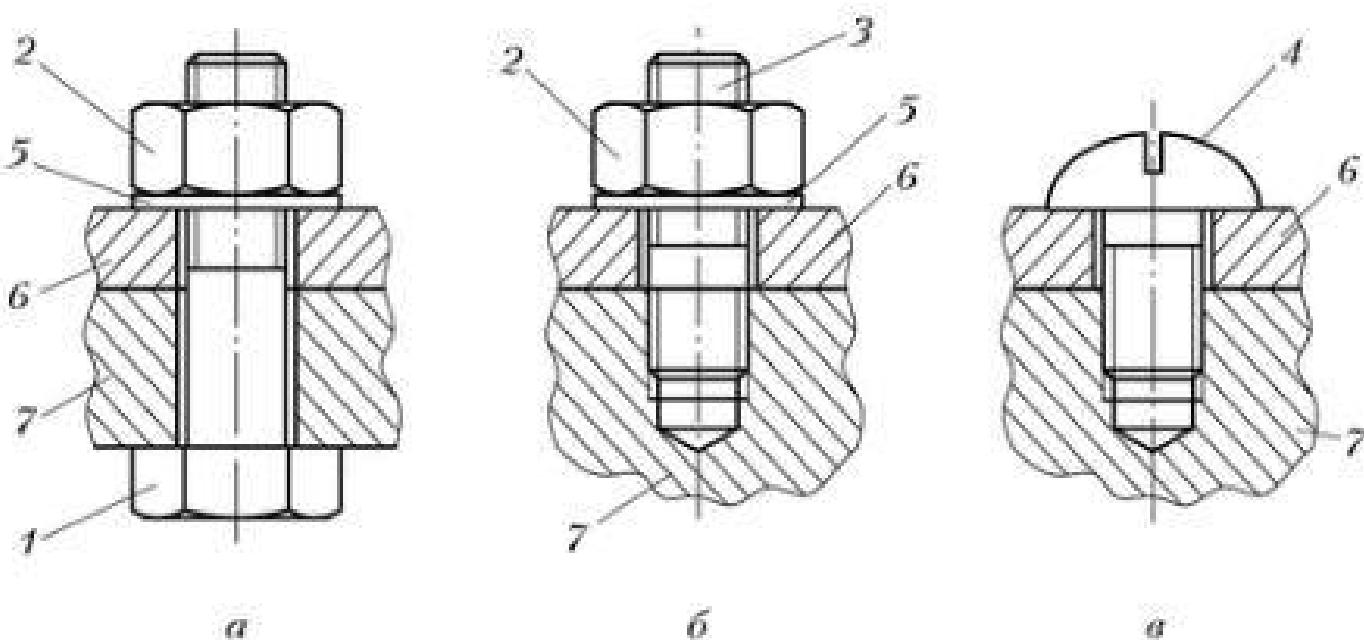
Резьбовые соединения: а – с помощью болта; б – с помощью шпильки; в – с помощью винта; 1 – болт; 2 – гайка; 3 – шпилька; 4 – винт; 5 – шайба; 6, 7 – соединяемые детали
